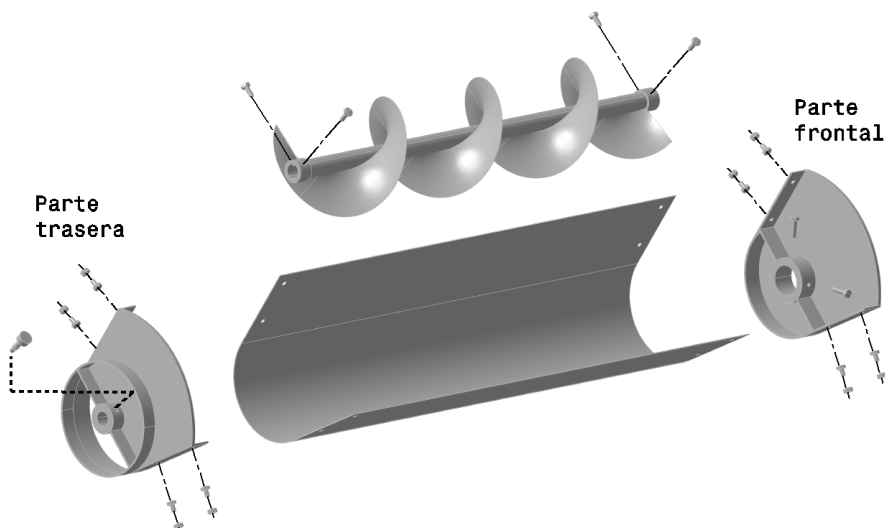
Vista explosionada del canalón y tornillo sin fin.
